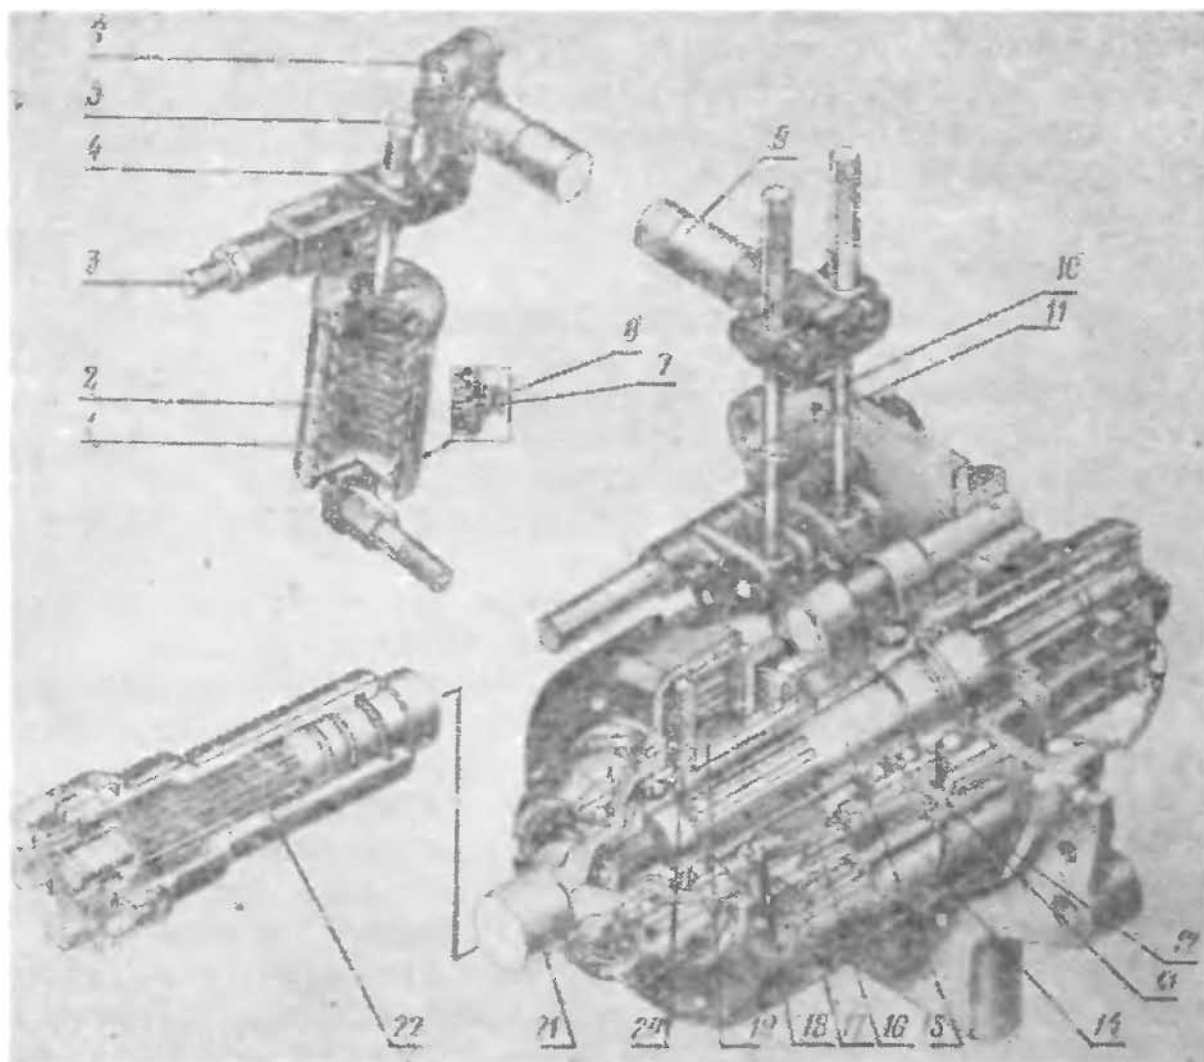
Планетарный редуктор заднего вала отбора мощности:
